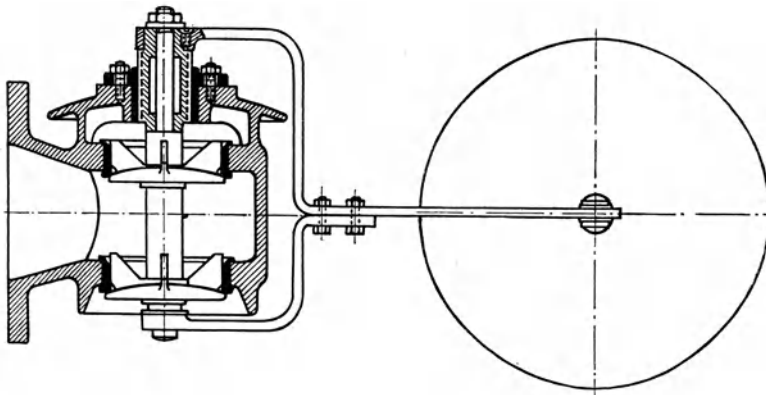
Innenliegendes Schwimmerventil mit Schraubenbewegung (Grundriß) (Schneider & Helmecke).
